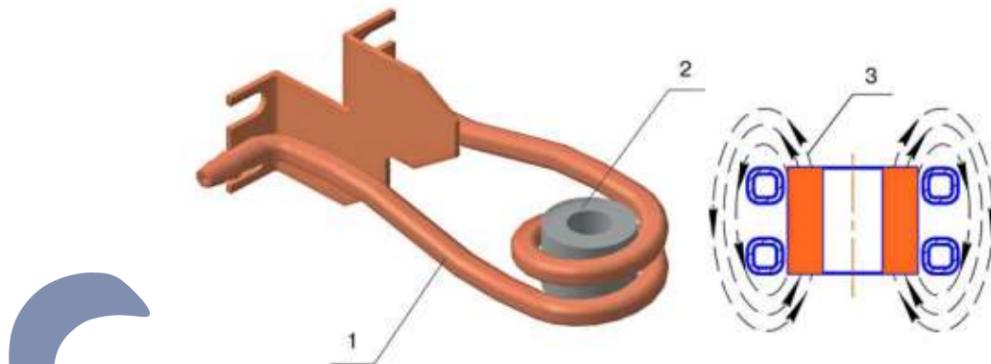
Схема індукційної системи нагріву деталі: 1 - індуктор; 2 - нагрівається заготовка; 3 - струми Фуко [19]
